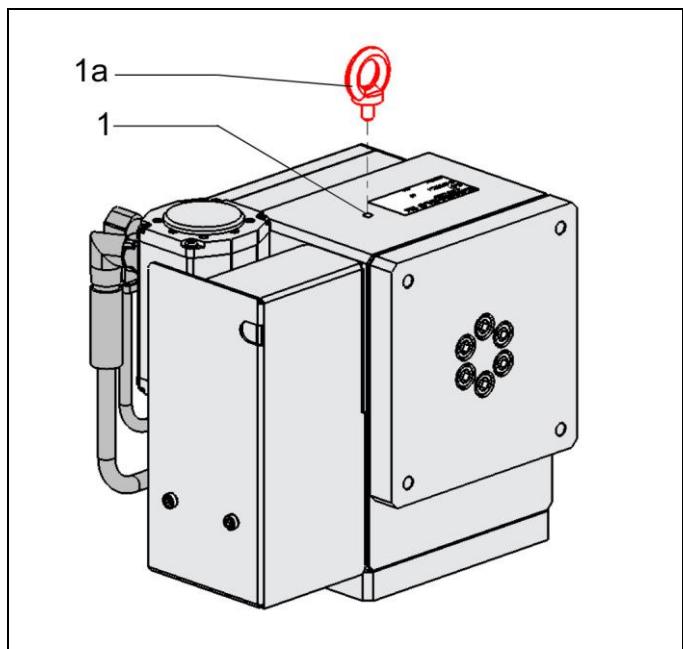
Punto para el izado mediante carretilla elevadora (ejecución horizontal 6508 0236 E)
